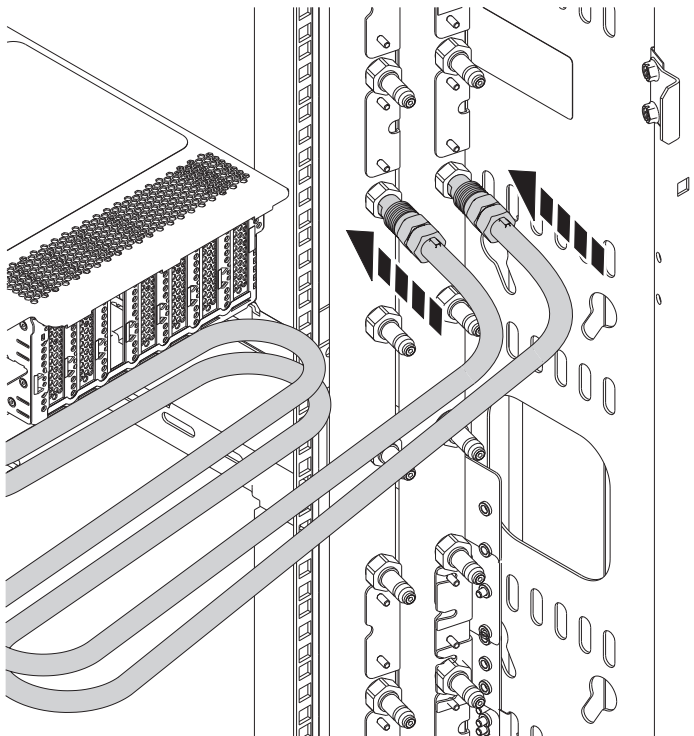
Schnellanschlüsse an dem Zulauf- und dem Rücklaufschlauch installieren
